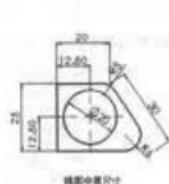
原尺寸及编辑尺寸公差精度后的尺寸
